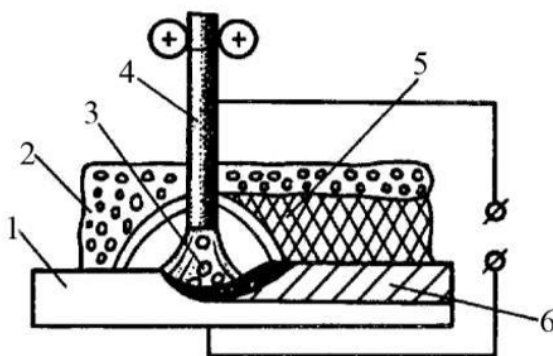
Схема процесса автоматической дуговой сварки под флюсом
